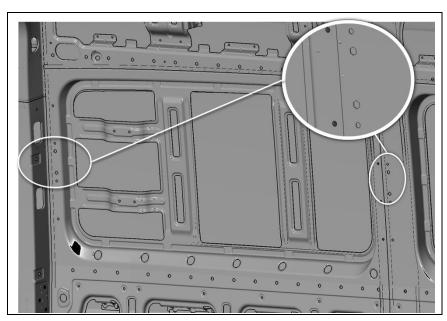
prééquipement d'étagères sur la carrosserie (panneau latéral), exemple : rail Airliner monté sur le panneau latéral
